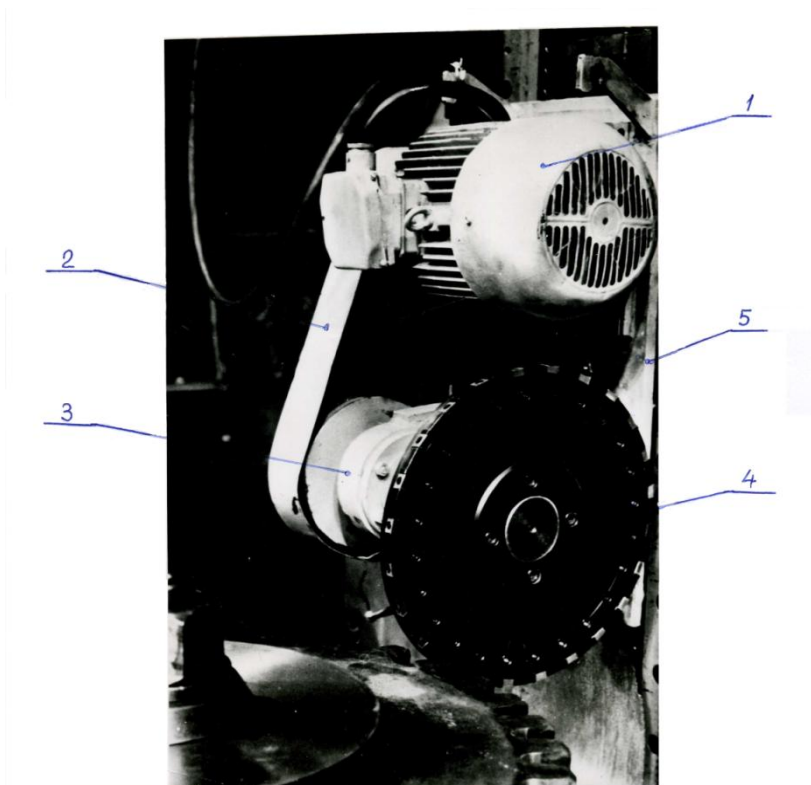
Робоча конструкція спец супорта до зубостогального верстата фірми «МАОГ»
